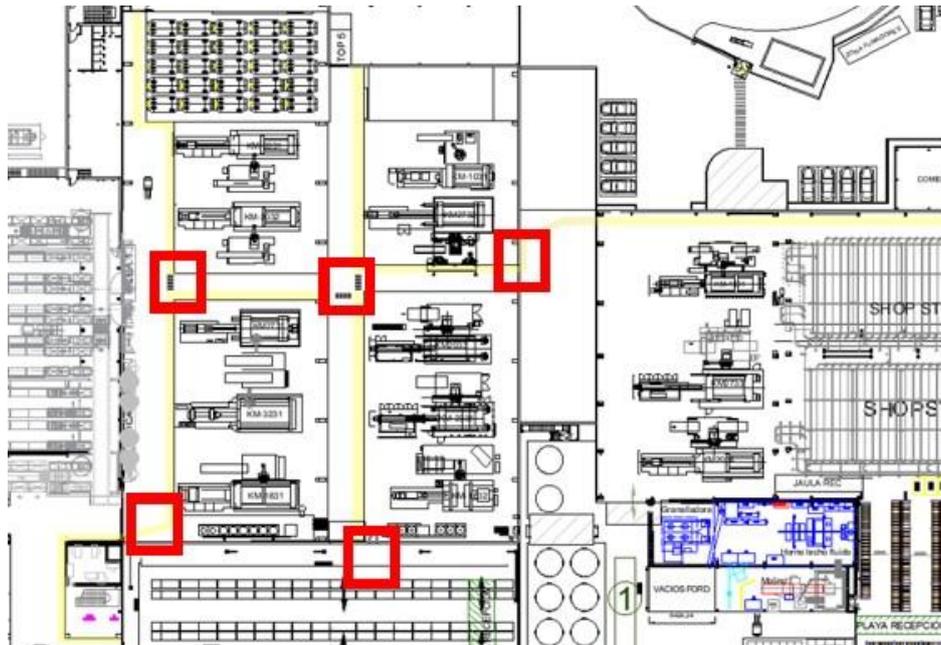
Layout de planta con los pasos de cebra destacados - Fuente: Documentación interna de la empresa (2021)
